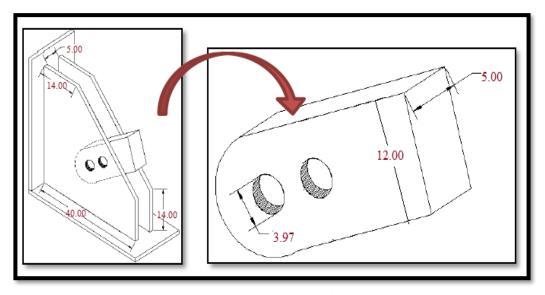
Detalle de la barra de conexión. Fuente: Propia.
